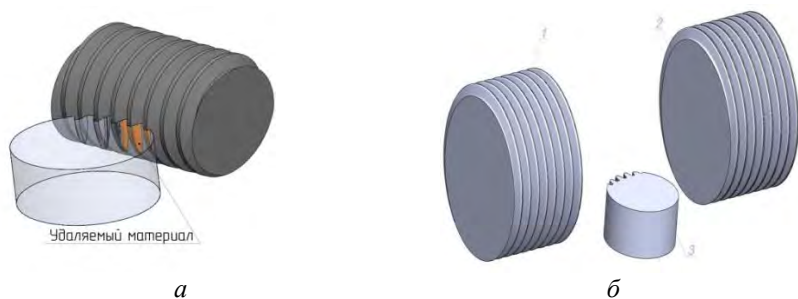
Виртуальная модель обработки зубчатого колеса:
